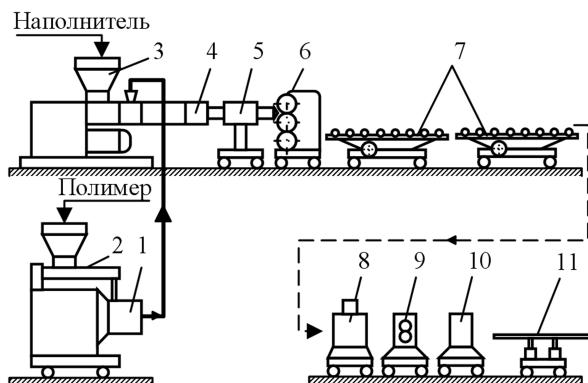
Схема технологической линии для производства древесно-полимерных листов: 1 — червячно-дисковый расплавитель; 2 — питатель полимера; 3 — дозатор наполнителя; 4 — двухчервячный экструдер; 5 — плоскощелевая экструзионная головка; 6 — трехвалковый гладильный каландр; 7 — охлаждающие устройства; 8 — устройство продольной резки; 9 — тянущее устройство; 10 — устройство поперечной резки; 11 — стопоровое устройство.
